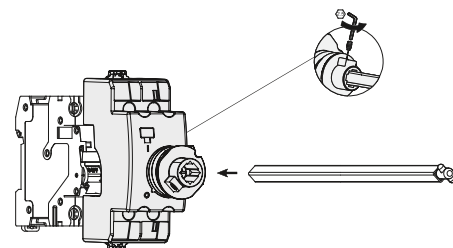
Монтаж и крепление металлического штока / Figure 8 – Mounting and securing the metal rod
